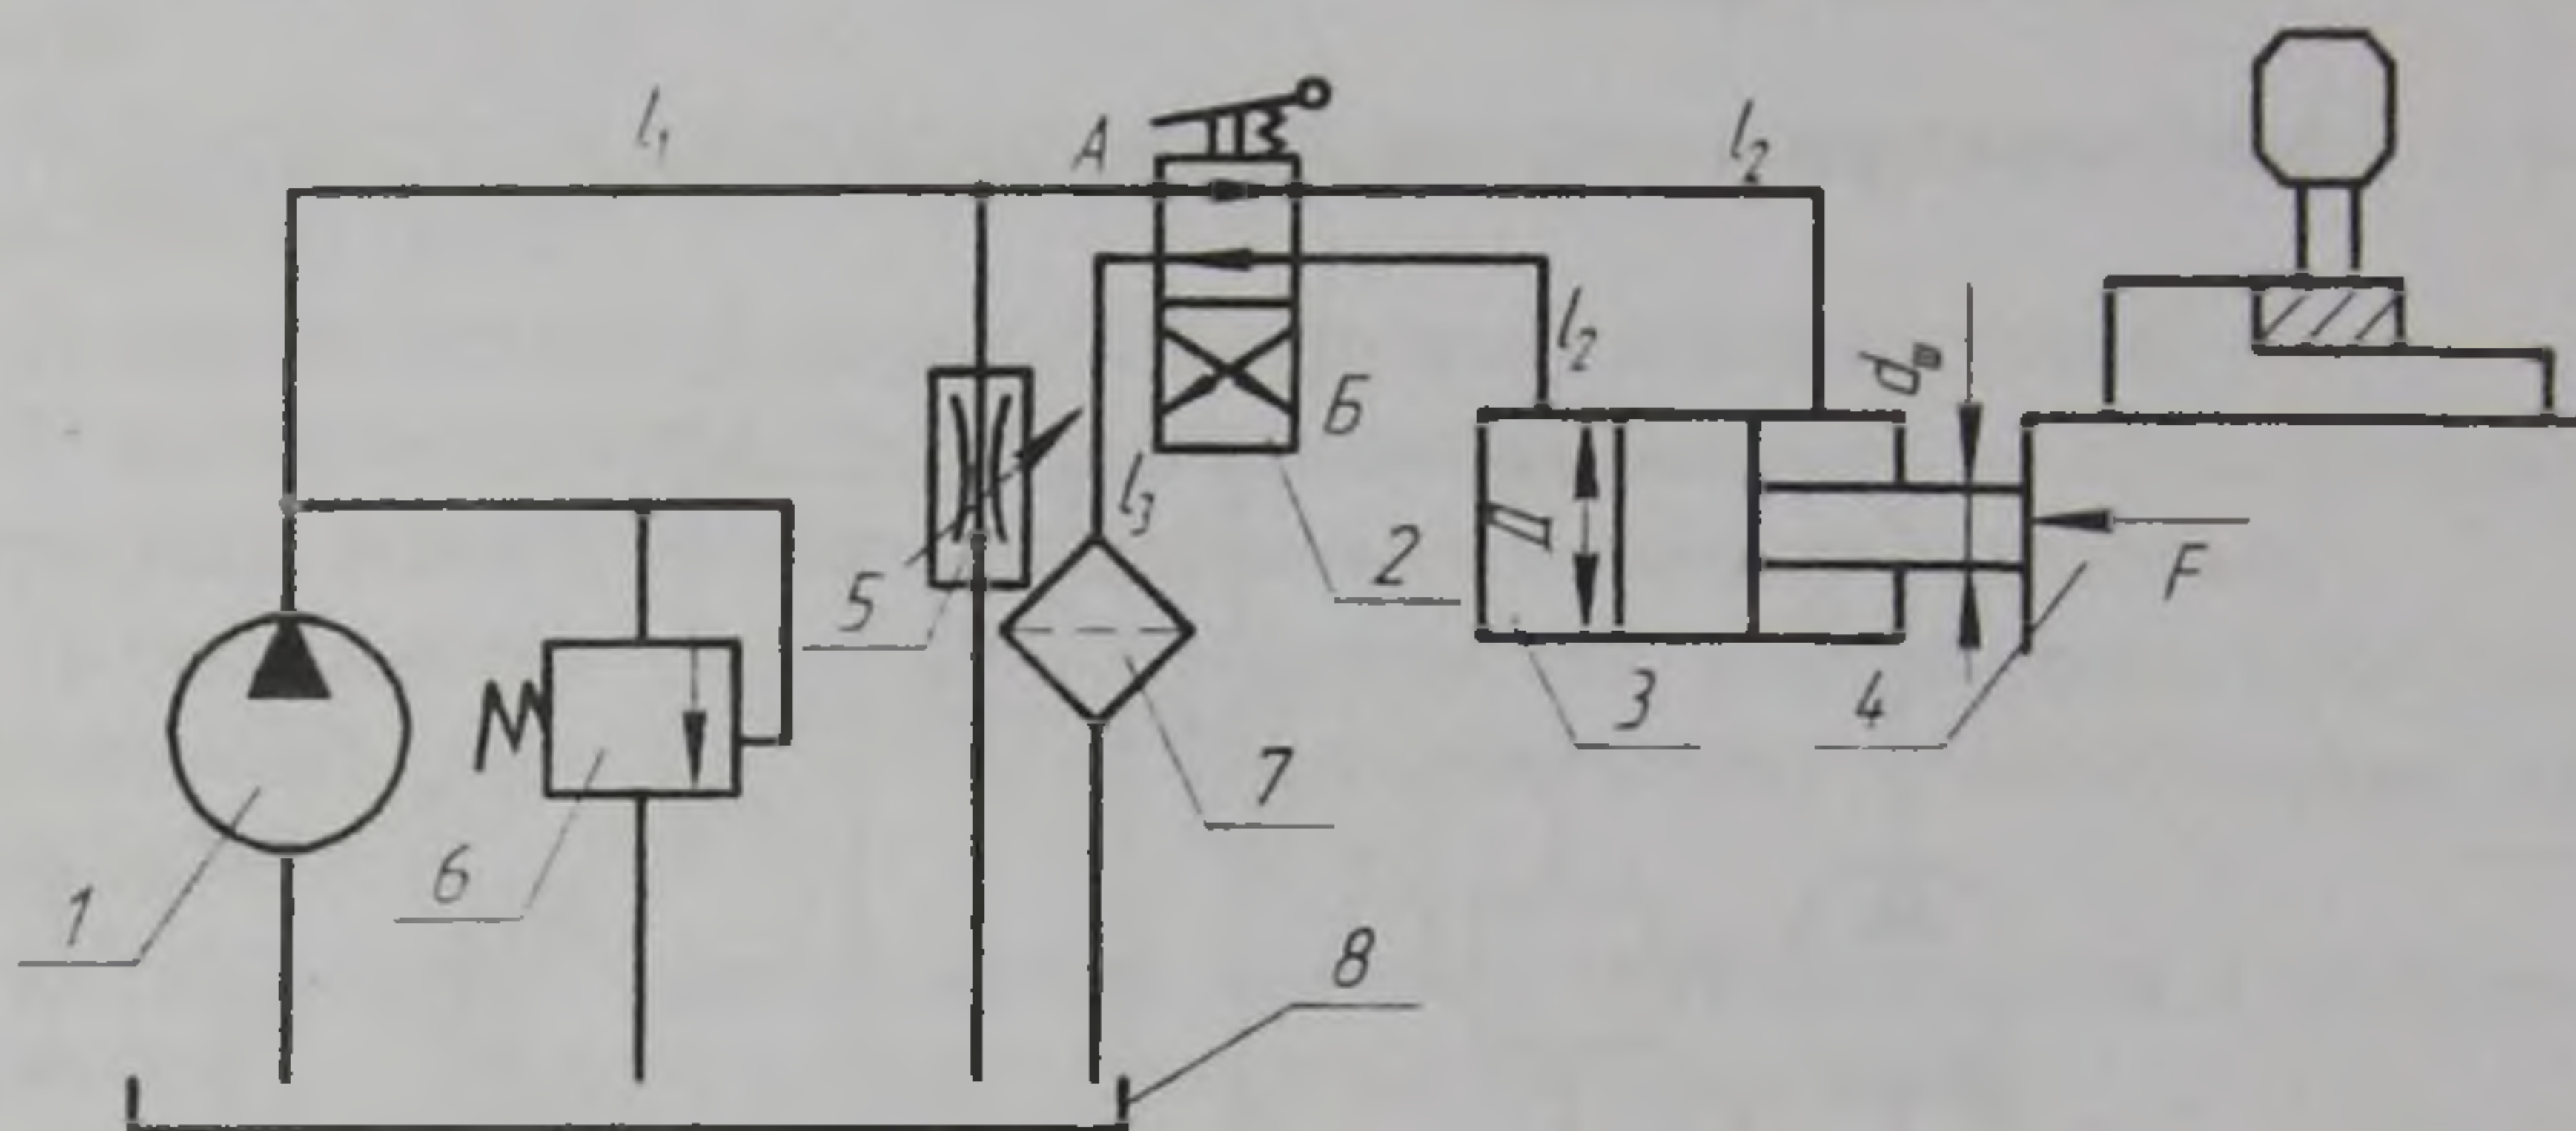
Схема гидропривода стола фрезерного станка
